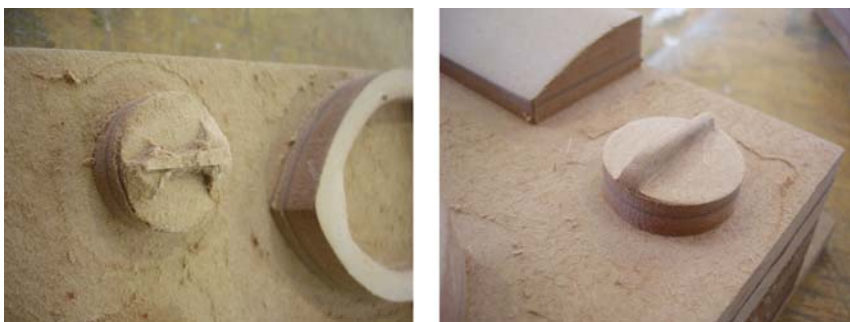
Processo de usinagem dos moldes. Fonte: Adriano de Luca.
